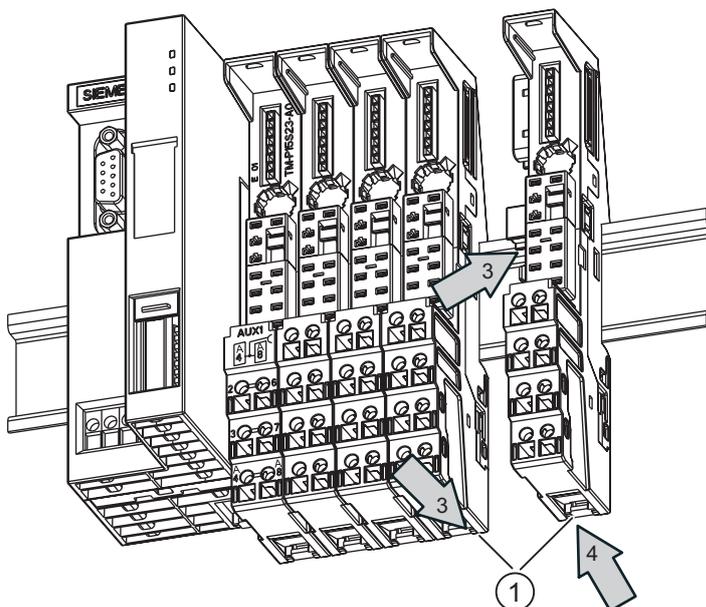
Desmontaje del módulo de terminales (por la derecha)
